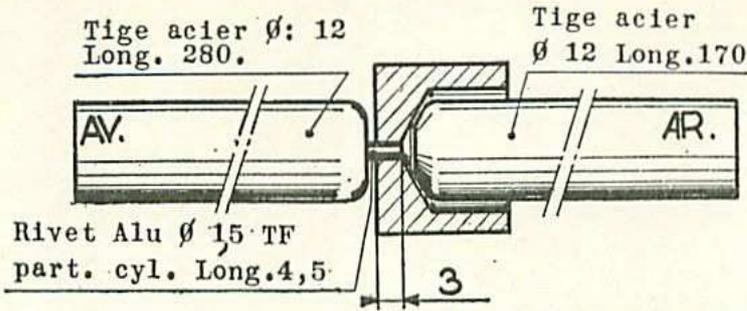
Obturer avec un rivet, le trou côté volant dans le vilebrequin.
